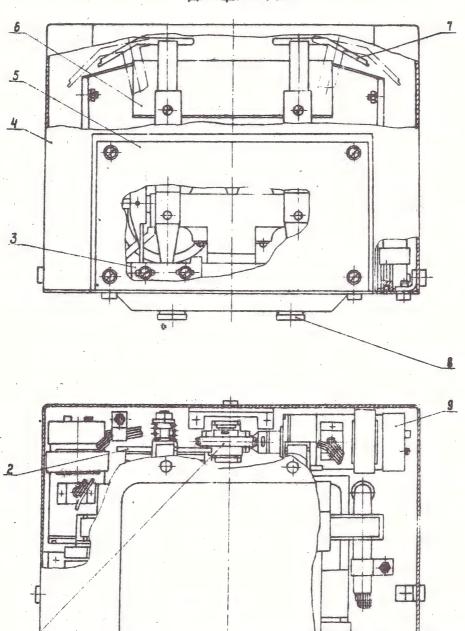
1-Редумтор; 2-Муфта: 3-Упор; 4-Кечтия, 5-Шторка: 6-Шторка: 8-Болт: 9-Электродвигатель
